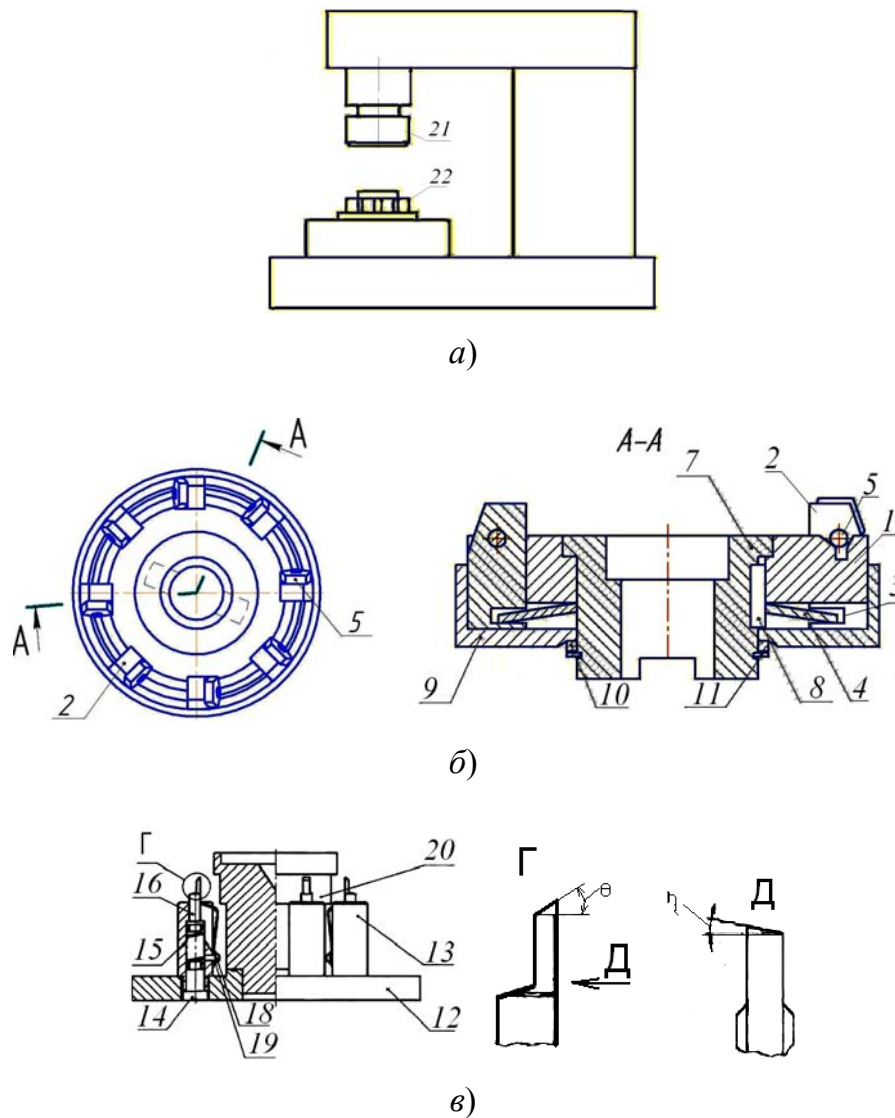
Эскизы устройства с автоматической сменой режущих кромок фрезы
